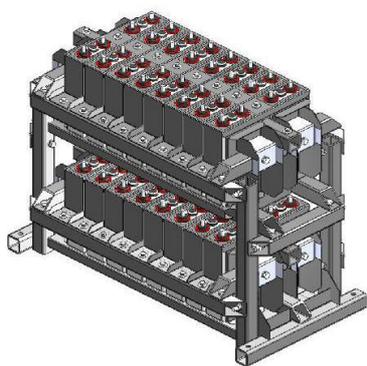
Внешний вид устройства СА-У1
